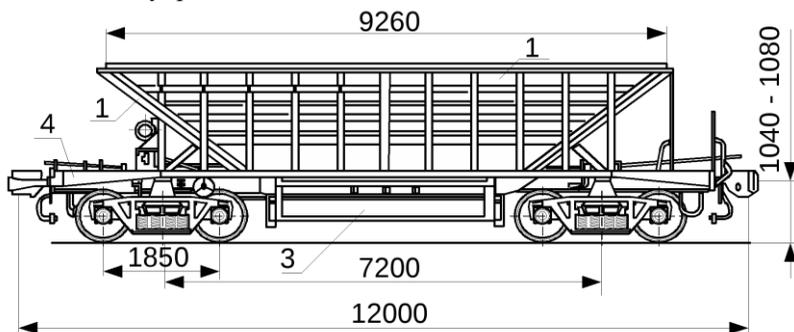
Специализированный саморазгружающийся бункерный полувагон-хopper
